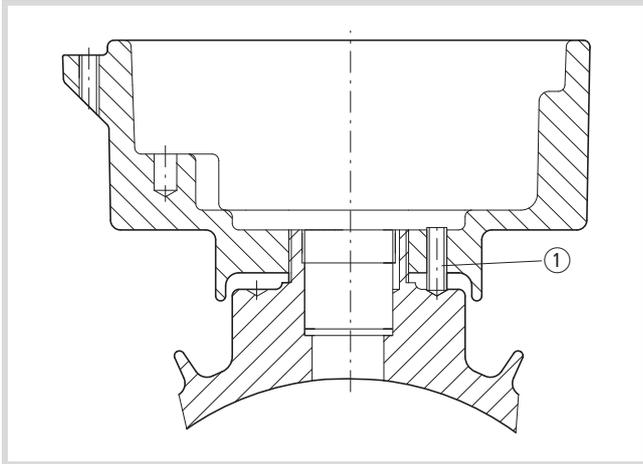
Klemmenkasten (6.01) über Gewinde befestigen
